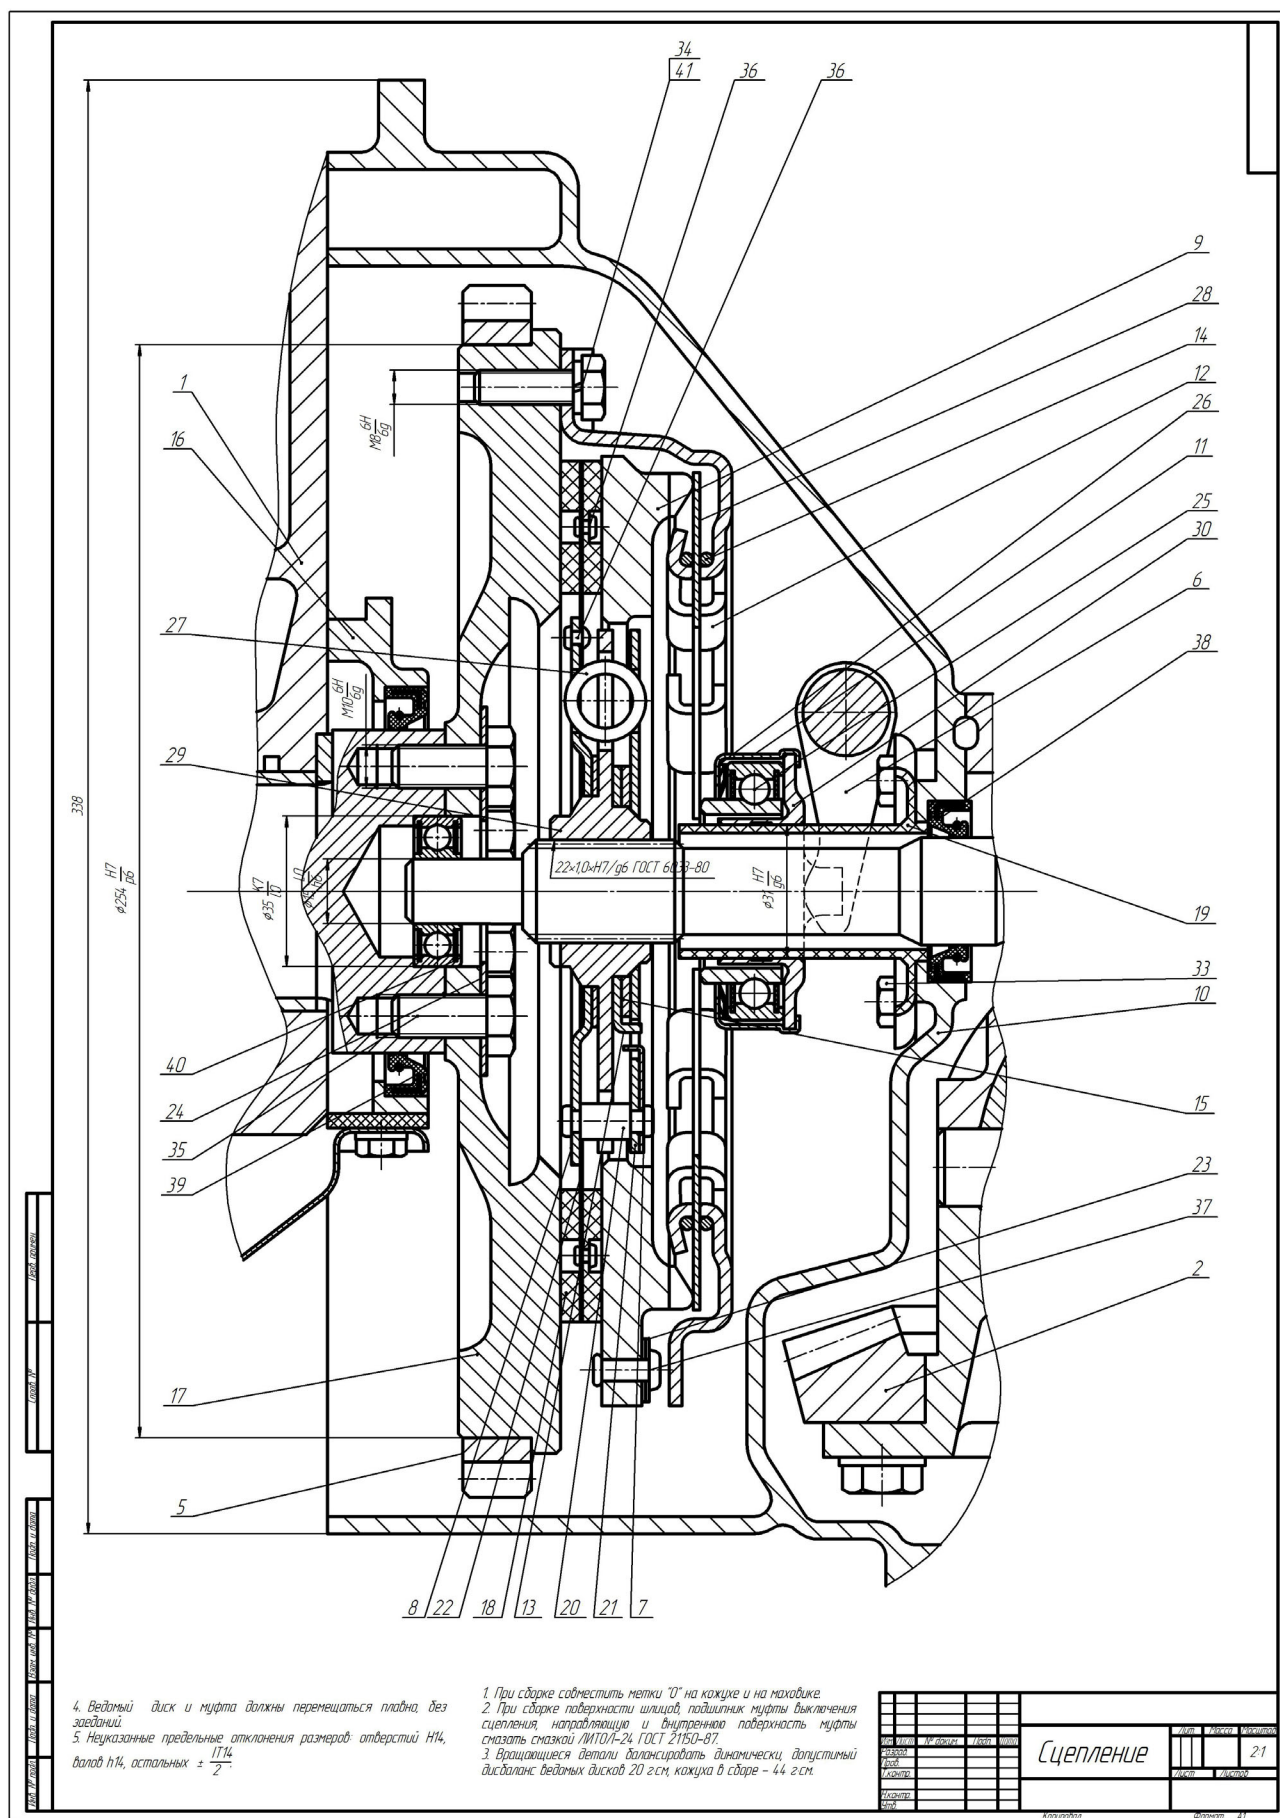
Пример выполнения сборочного чертежа сцепления
